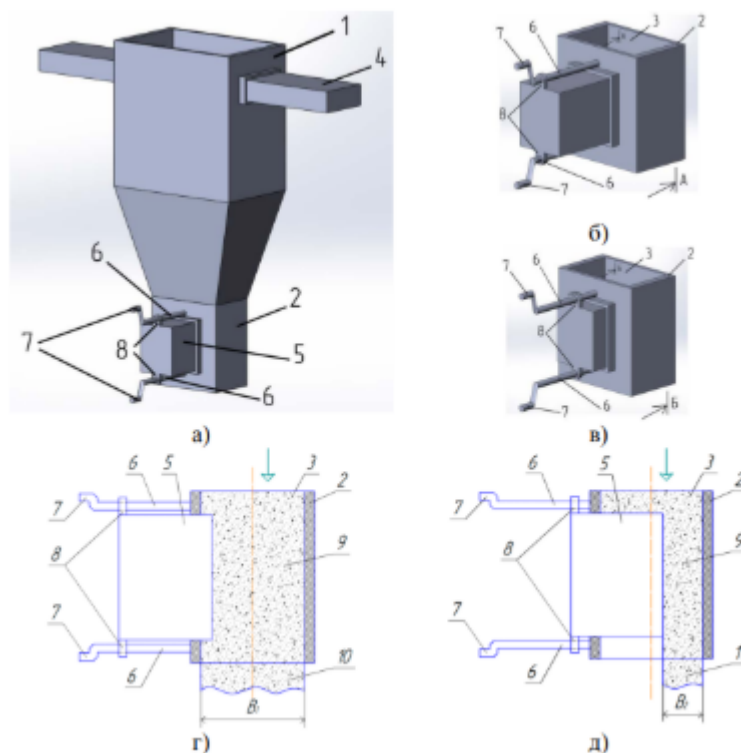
Головка друку із змінною шириною шару бетону: а) — загальний вигляд; б) ... д) — екструдер з різними положеннями вкладки. 1 — корпус; 2 — екструдер; 3 — направляюча; 4 — направляюча; 5 — вкладка; 6 — гвинт; 7 — рукоятка; 8 — гайка; 9 — суміш; 10, 11 — шар бетону
